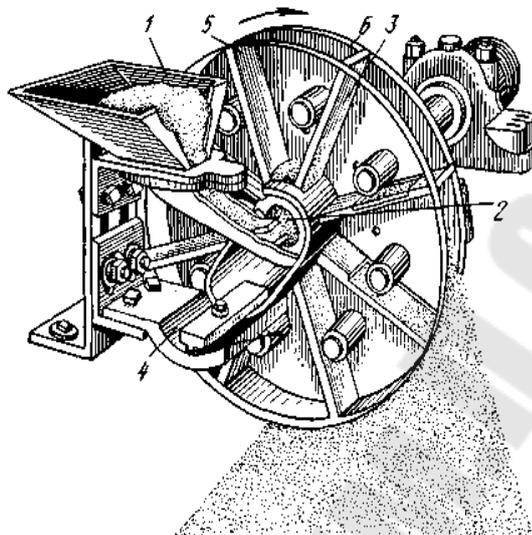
Принцип действия лопаточного дробеметного колеса: 1-воронка с дробью; 2-лопатки распределительного колеса; 3- окно во втулке распределительного колеса для выхода дроби (импеллера); 4- втулка (труба), ограждающая импеллер; 5- рабочие лопатки колеса; 6- диски колеса
